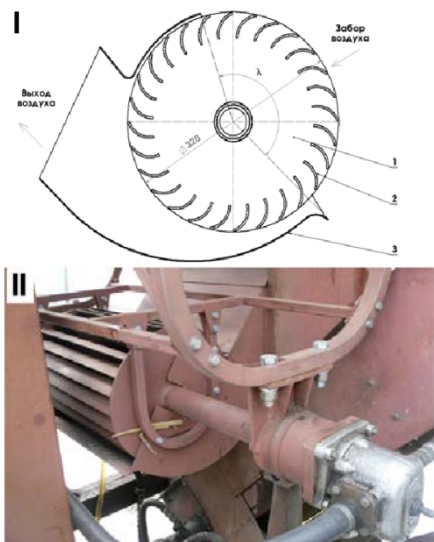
I – схема диаметрального вентилятора: 1 – диск; 2 – лопатка; 3 – кожух; II -- диаметральный вентилятор на комбайне
